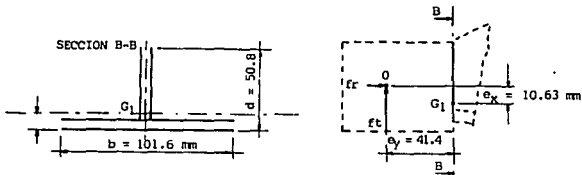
Dimensiones de la sección B-B de las soldaduras.
